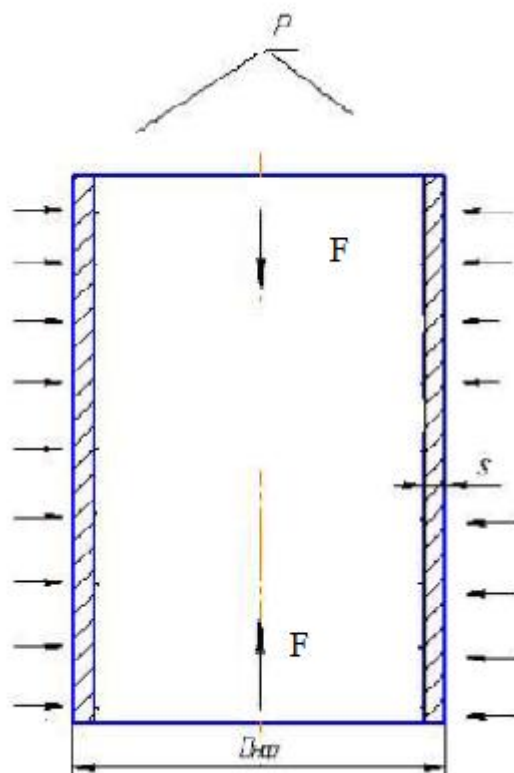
Расчетная схема цилиндрической обечайки №1
